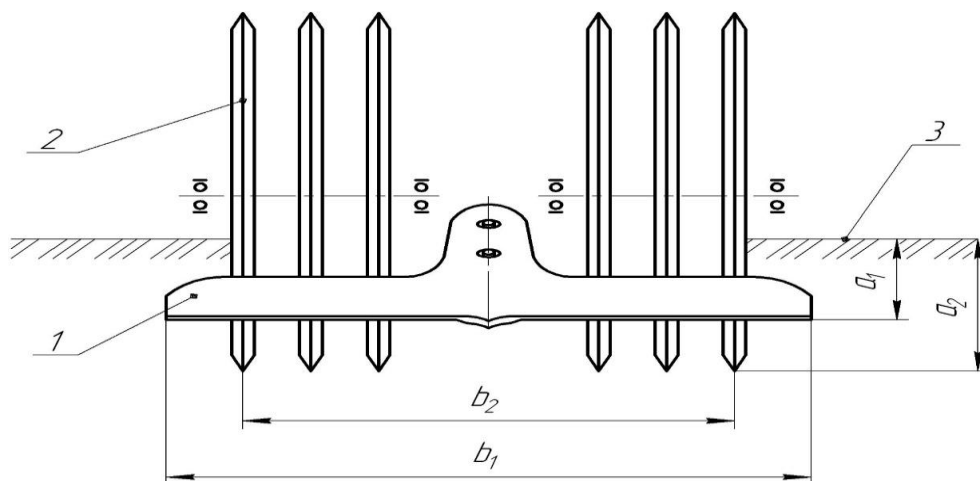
Розрахункова схема комбінованого агрегату [6] : 1 – лапа стрільчаста; 2 – дискова батарея; 3 – рівень денної поверхні
